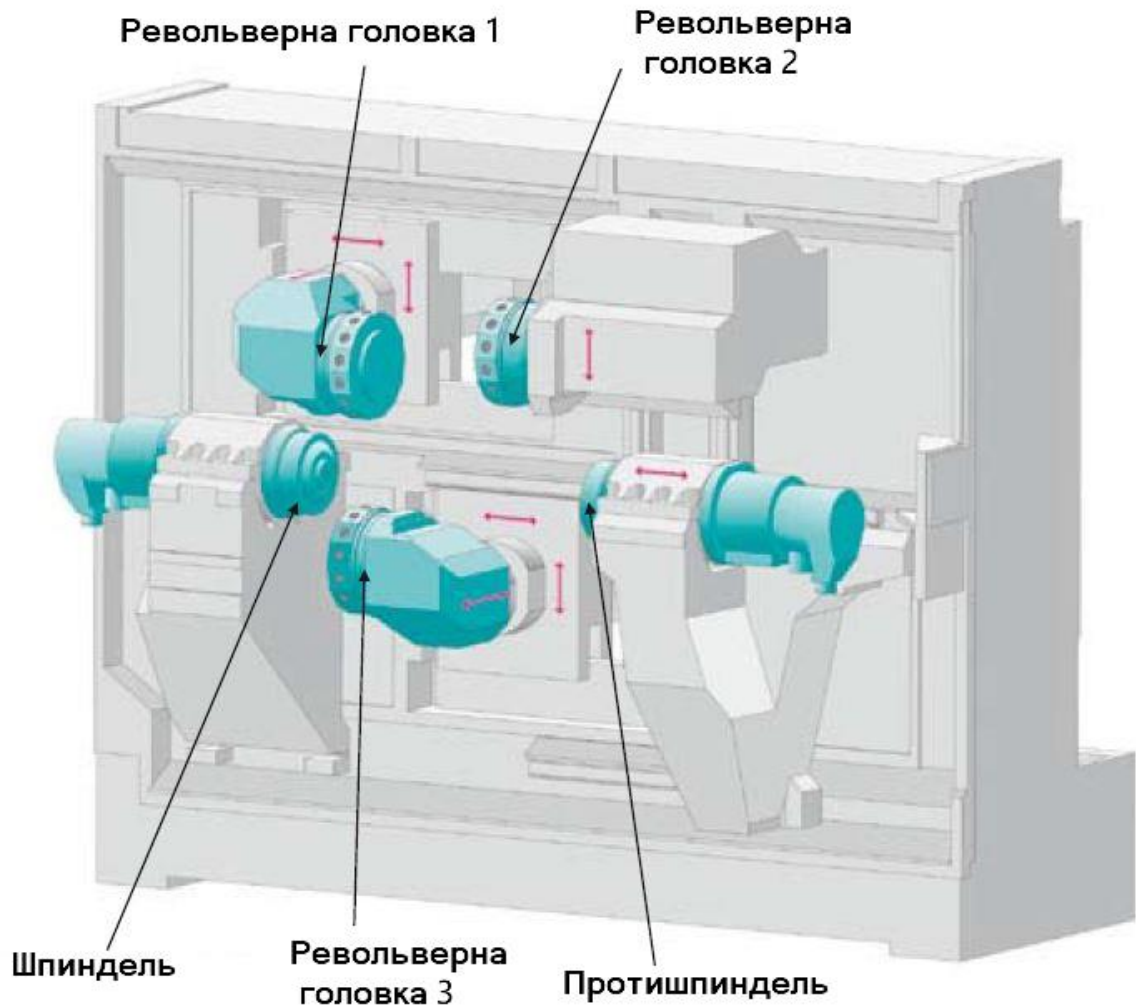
Компонування багатшпиндельного токарного верстата з ЧПК INDEX C100
